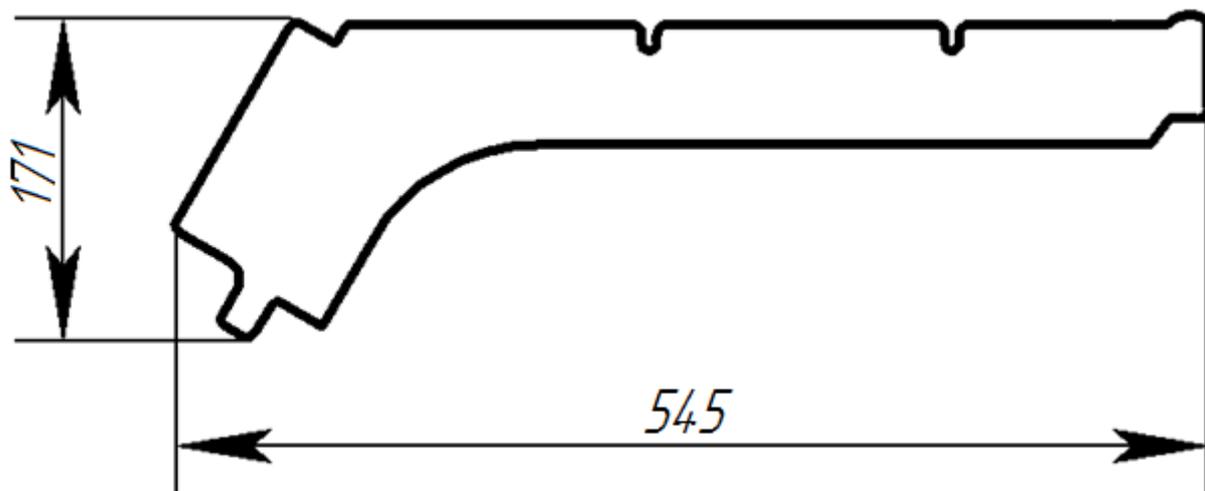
Эскиз заготовки элемента шпангоута
